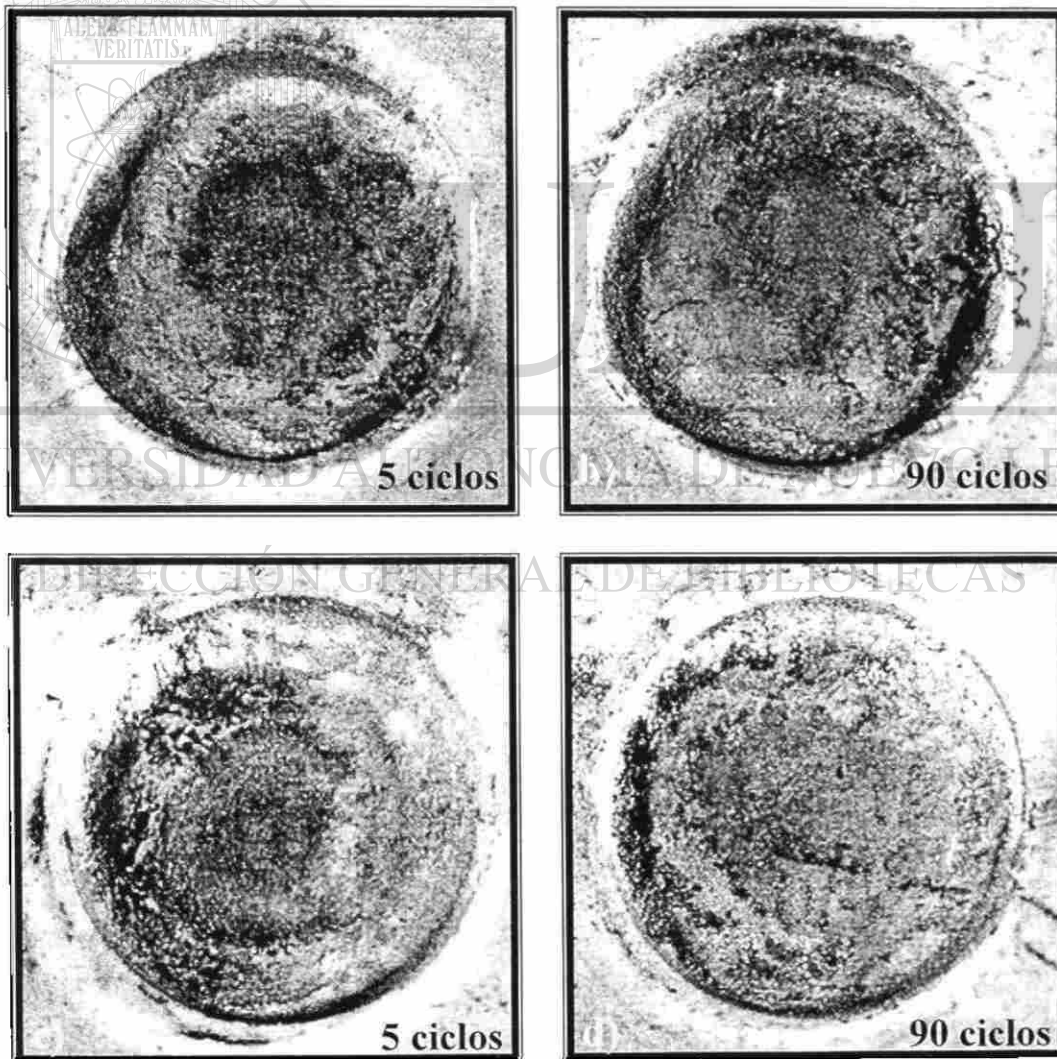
Aspecto superficial de los puntos de soldadura. a) y b) bajo Sb; c) y d) alto Sb. a) Panel 1, punto 7. b) Panel 3, punto 4. c) Panel 1, punto 5. d) Panel 3, punto 1.
